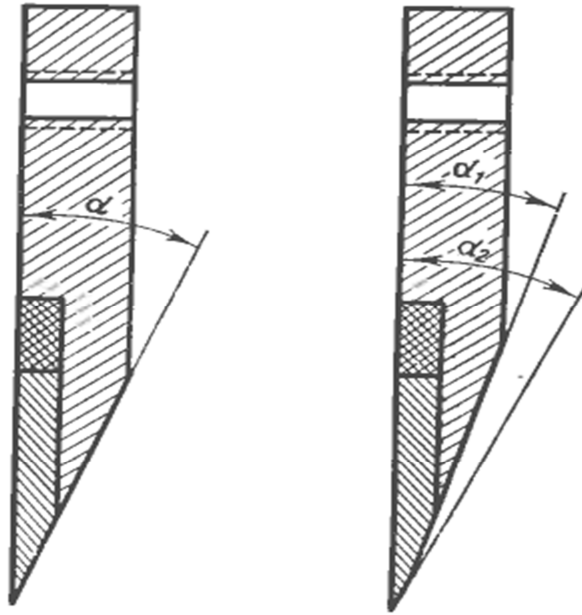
Різновиди заточування ножів машин для різання друкованих заготовок упаковки
